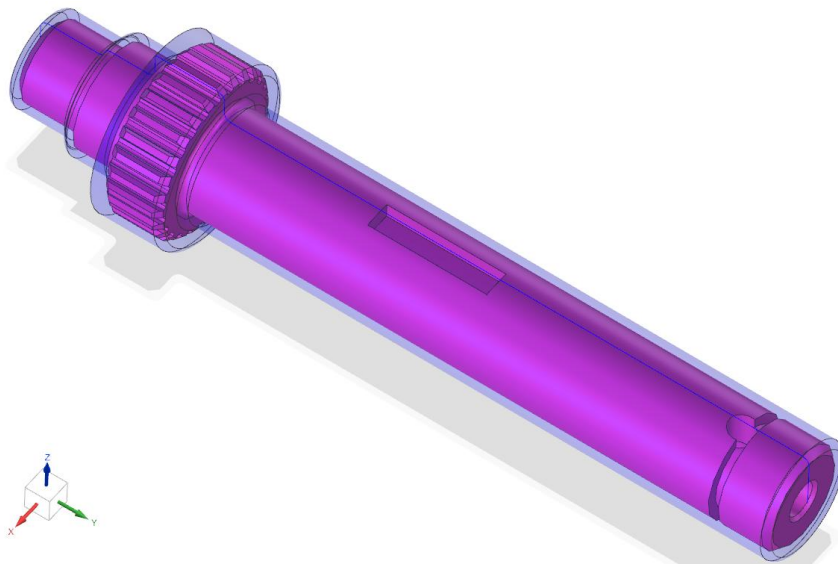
Суміщення 3-D моделі робочої деталі та заготовки
